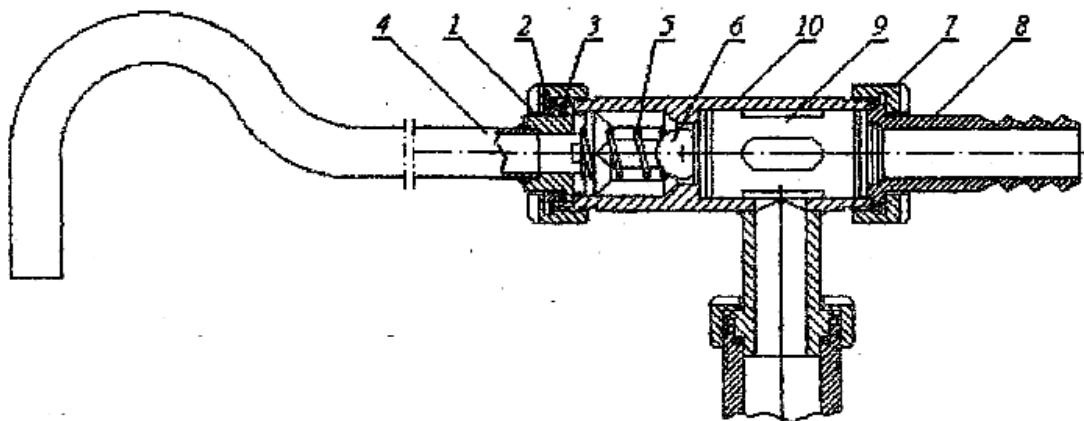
Схема розташування деталей в корпусі клапана: (розбирання клапана вести в черговості за номерами позицій на кресленні) 1 – гайка; 2 – кільце; 3 – прокладка; 4 – патрубок; 5 – пружина; 6 – кулька; 7 – гайка; 8 – ніпель; 9 – гільза; 10 – корпус клапана
